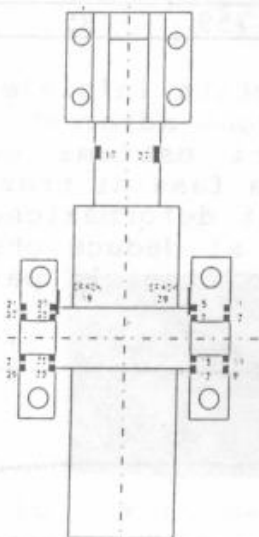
Disposizione degli estensimetri e del crack gauge.
